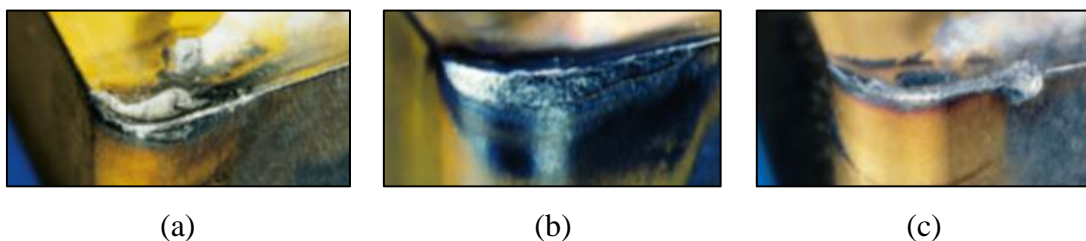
Os três desgastes típicos de ferramentas de corte, a) Cratera, b) Flanco e c) Entalhe. [10]
